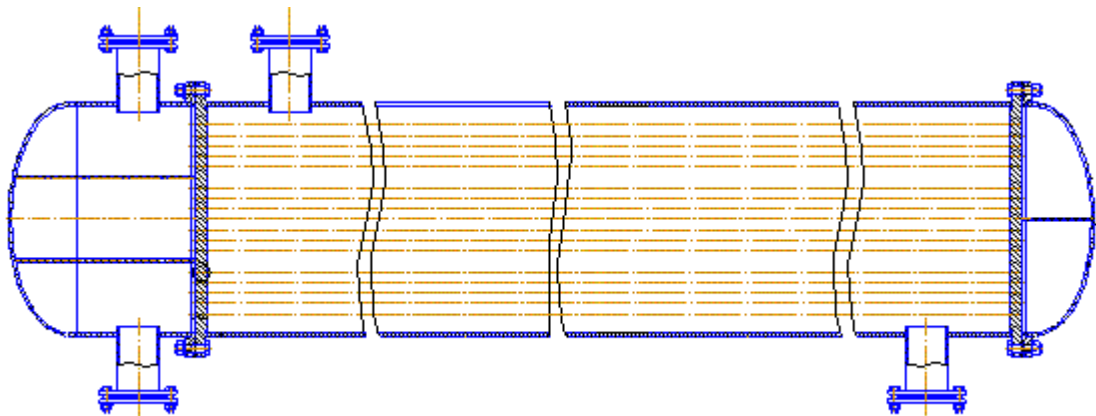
Конструктивна схема кожухотрубного конденсатора
